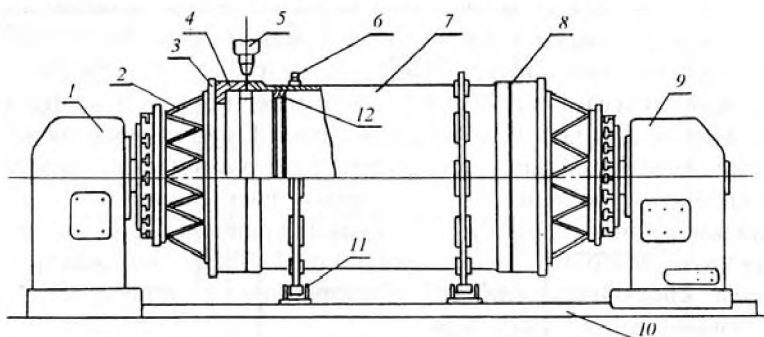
Схема двухопорной установки для сварки колец: 1 – неподвижная бабка стапеля; 2 – корзина; 3 – переходное кольцо; 4 – торцевой шпангоут; 5 – сварочная горелка; 6 – бандаж; 7 – обечайка; 8 – сварной шов; 9 – неподвижная бабка; 10 – направляющие; 11 – катки; 12 – разжимное кольцо
